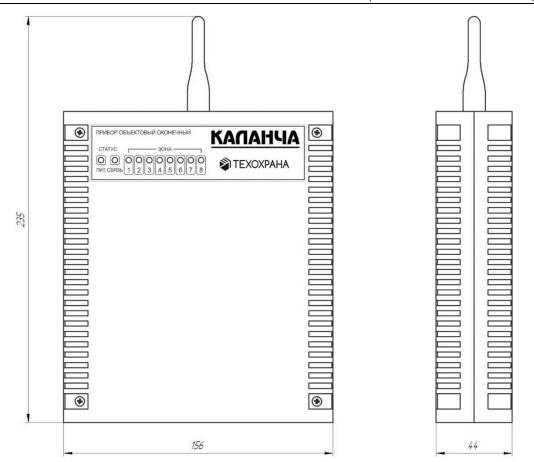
Внешний вид и установочные размеры ПОО «Каланча»
